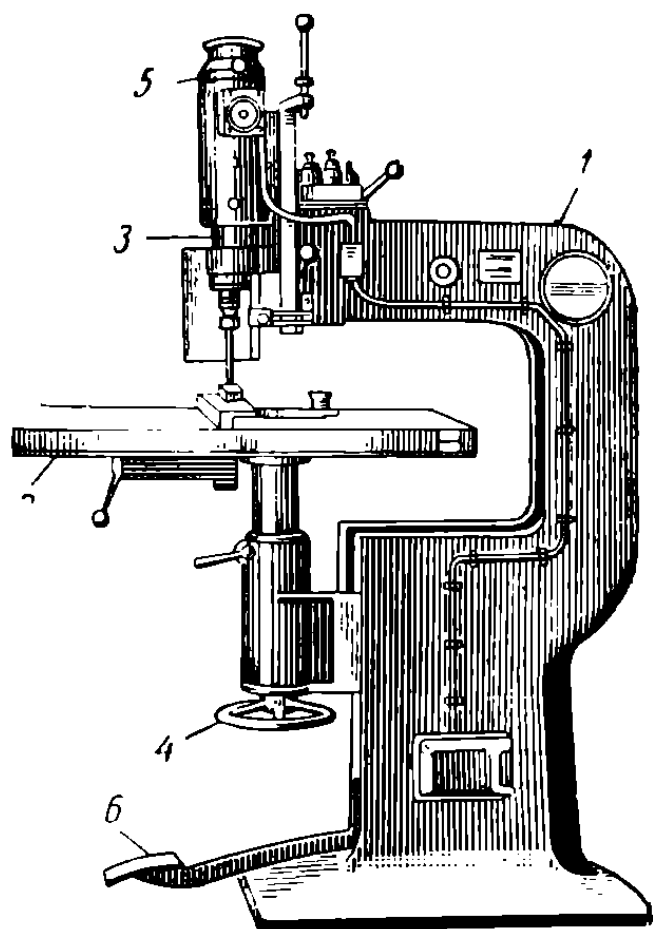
Фрезерно-копировальный станок с верхним шпинделем:
